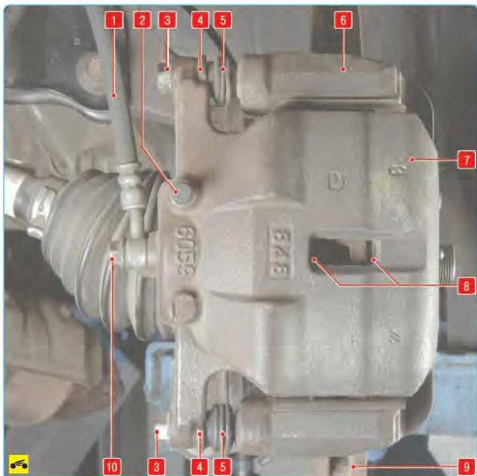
Тормозной механизм переднего колеса 1 – тормозной шланг; 2 – клапан выпуска воздуха; 3 – болт крепления направляющего пальца суппорта; 4 – направляющий палец суппорта; 5 – пыльник направляющего пальца; 6 – направляющая колодок; 7 – суппорт тормозного механизма; 8 – тормозные колодки; 9 – тормозной диск; 10 – болт шпигота тормозного шланга
